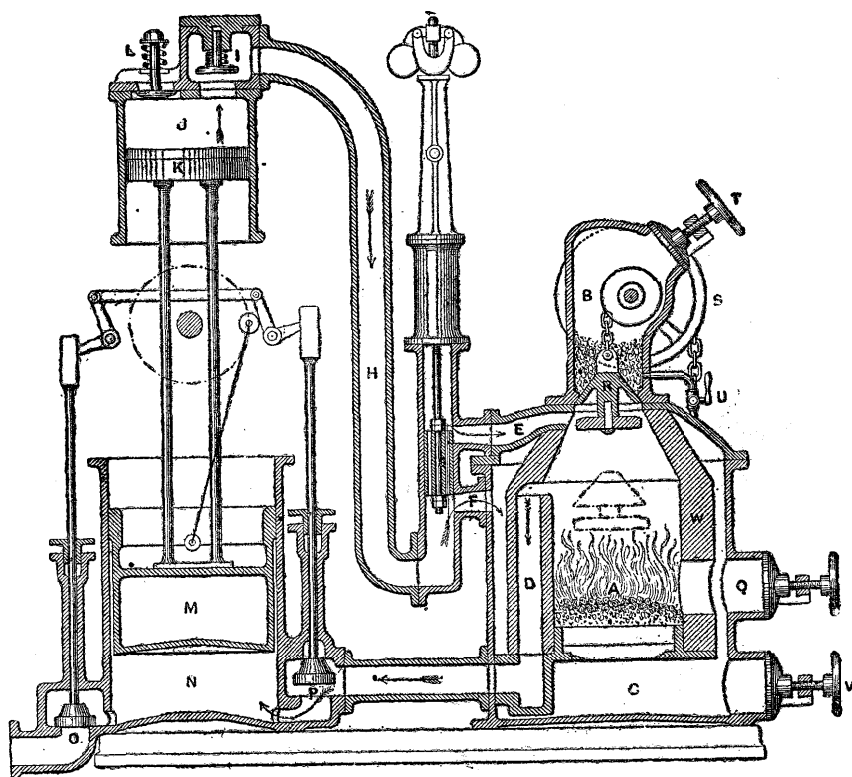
Machine Buckett de 15 chevaux.* — A, foyer clos recevant l'air comprimé par la pompe J, dans le tuyau H, par une valve de réglage G, soumise au régulateur; cette valve admet, suivant sa position, une partie plus ou moins grande de l'air au-dessus de la grille par GE, et le reste au-dessous, pour activer plus ou moins la combustion suivant l'allure du moteur. B, trémie de chargement, dont le clapet R est commandé de l'extérieur par une manette S. U, robinet permettant de mettre en équilibre de pression la trémie B et le foyer. TQV, regards étanches de la trémie du foyer et du cendrier. PO, soupapes d'admission et d'échappement du cylindre moteur N. La soupape P, souvent en graphite, est rafraîchie par une circulation d'air froid non indiquée sur la figure. M, piston moteur, épais et non conducteur, relié directement au piston K de la pompe à air. L, aspiration, I, refoulement de la pompe à air.
